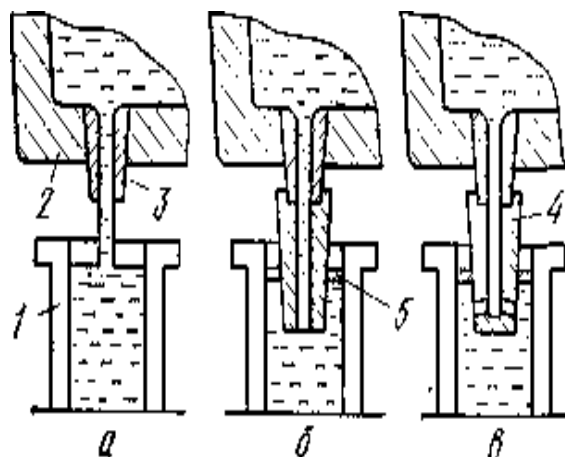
Способы подачи металла в кристаллизатор (обозначения в тексте)
